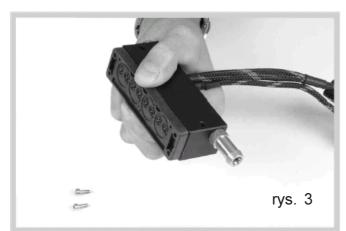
uszczelki o-ring znajdujące się na wsporniku zworów za pomocą szczypiec.
